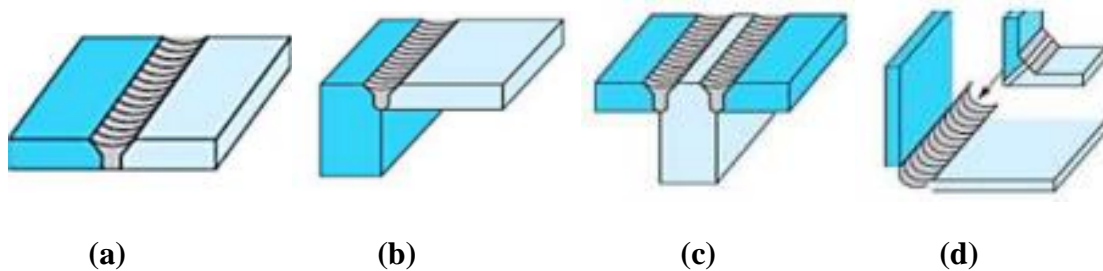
Les différentes configurations de soudage effectuées par FSW : (a) bout à bout, (b) en coin, (c) en T, et (d) angle [30]
